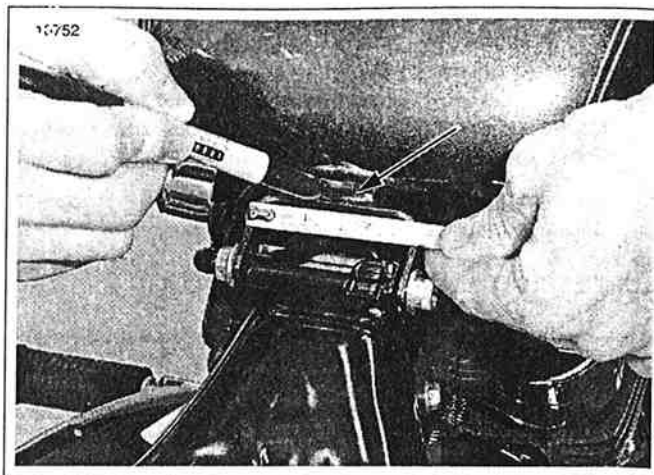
Marcado de la línea del centro del tanque de combustible
